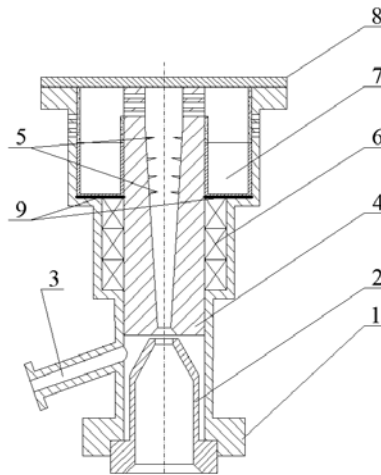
Ротаційний пиловіддільник: 1 – корпус; 2 – сопло високонапірного потоку; 3 – патрубок низьконапірного потоку; 4 – дифузор; 5 – лопаті дифузору; 6 – підшипники; 7 – циліндричний фільтр; 8 – кришка пиловіддільника; 9 – герметичне ущільнення; 10 – отвори у дифузори; 11 – отвори у корпусі.
